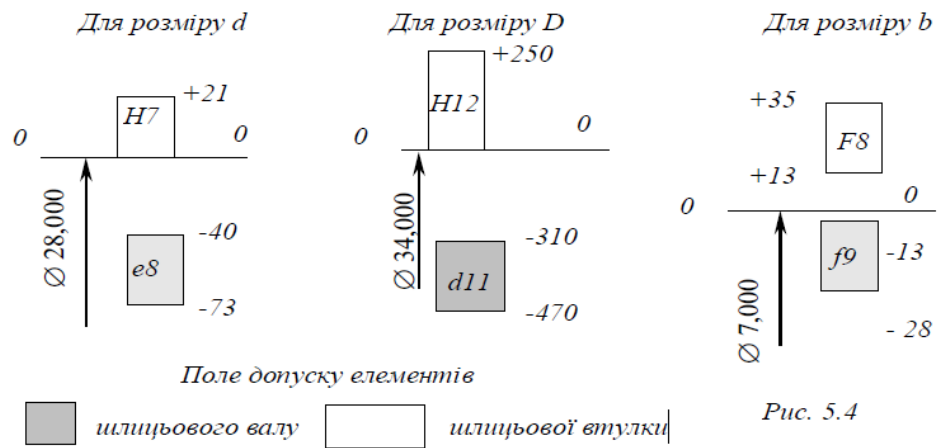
Схеми розташування полів допусків шліцевого з'єднання
